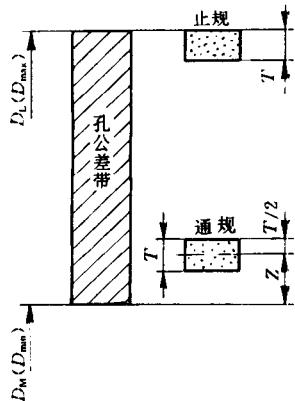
孔用工作量规定形尺寸公差带示意图
